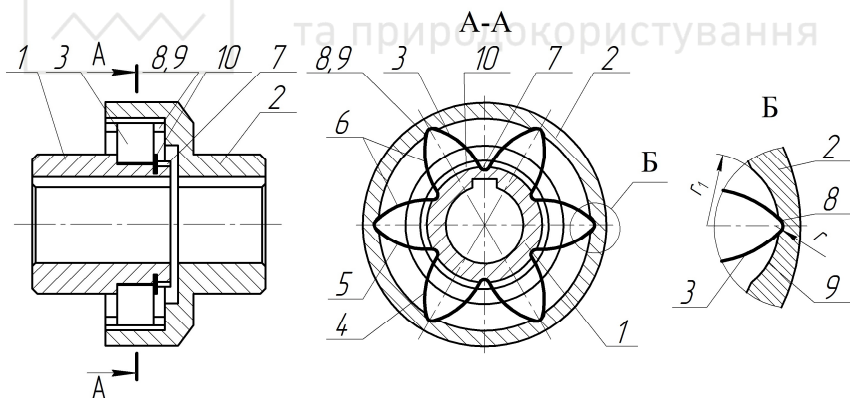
Муфта пружна зіркоподібною пружиною з різними радіусами заглиблень
